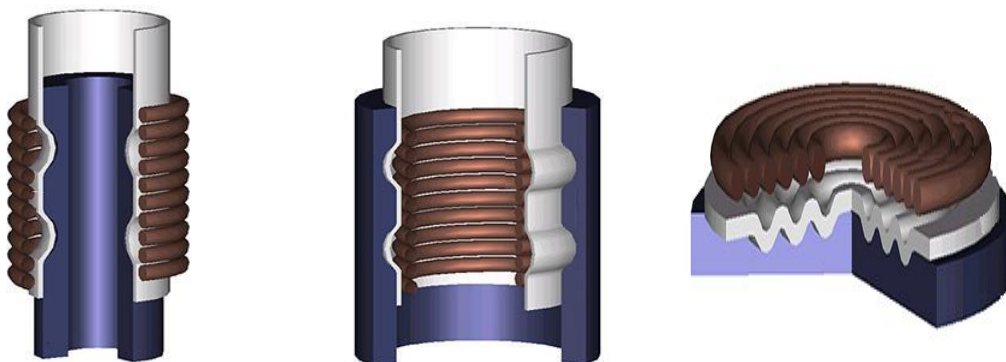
Bobines d'assemblage par impulsion magnétique [21]
